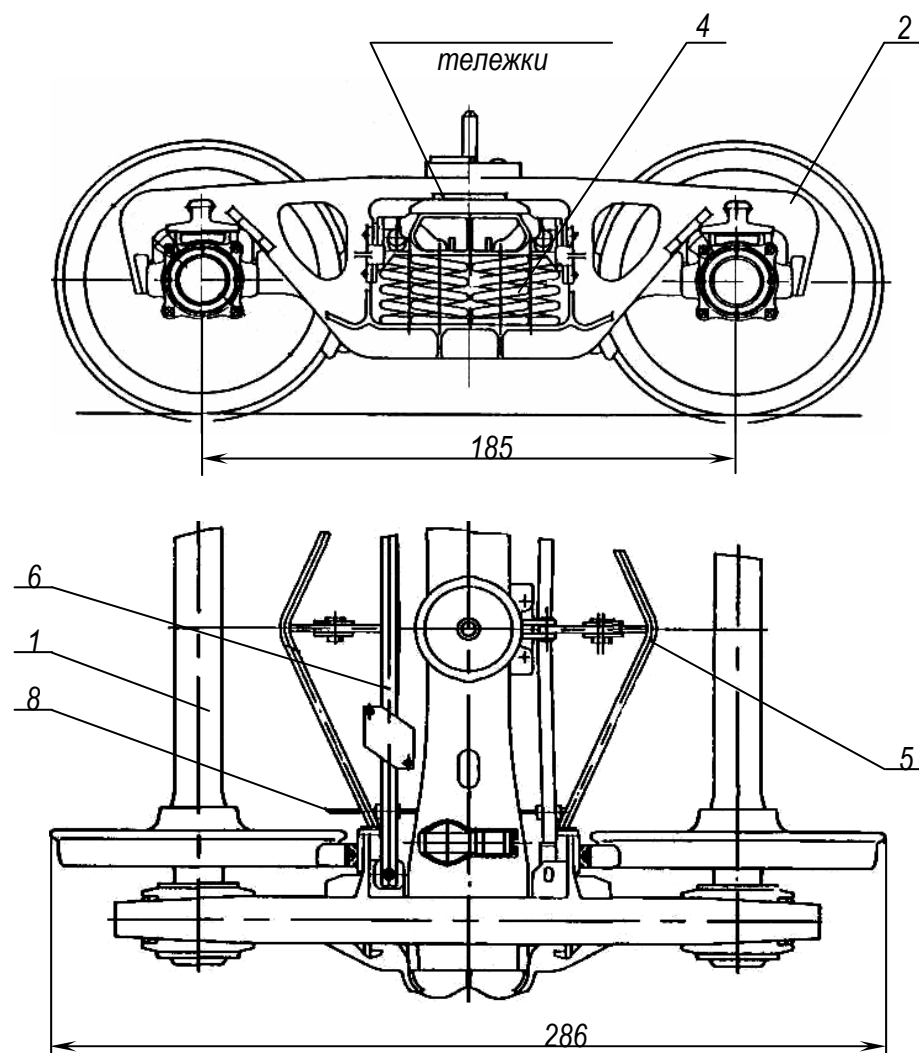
Тележка двухосная модель 18-578: 1 – колесная пара с буксовыми узлами; 2 – рама боковая; 3 – балка надрессорная; 4 – рессорное подвешивание; 5 – тормозная рычажная передача; 6 – опорная балка авторежима; 7 – скользящий; 8 – устройство направленного отвода колодок; 9 – шкворень
